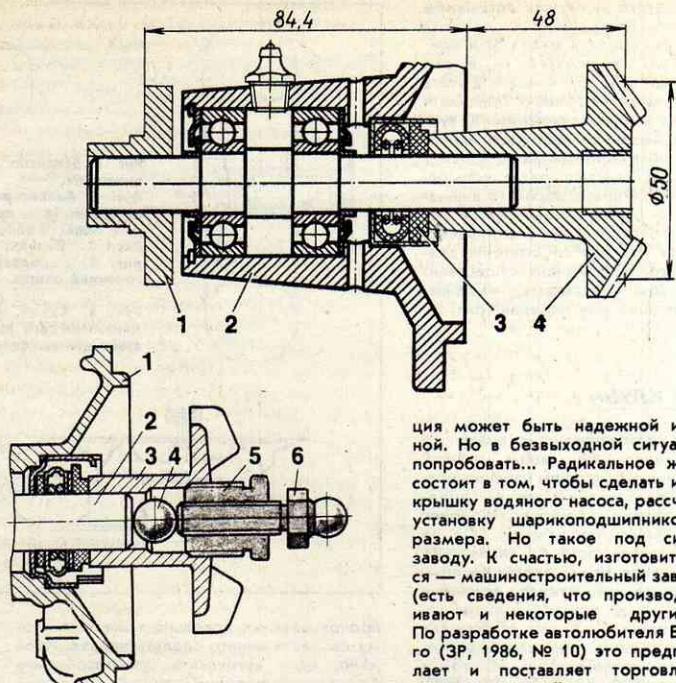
Съемник крыльчатки из деталей собственного мотора: 1 — крышка водяного насоса; 2 — валик; 3 — крыльчатка; 4 — шарик; 5 — втулка регулировки клапана; 6 — регулировочный болт.
